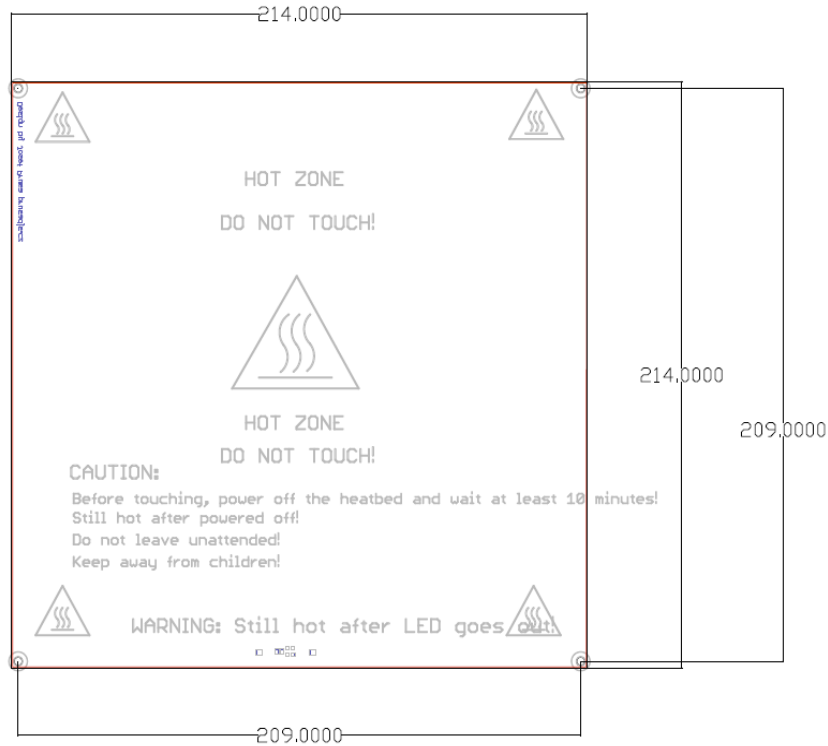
57. Dimensiones en mm de la cama caliente MK2. Fuente: *RepRap Wiki
